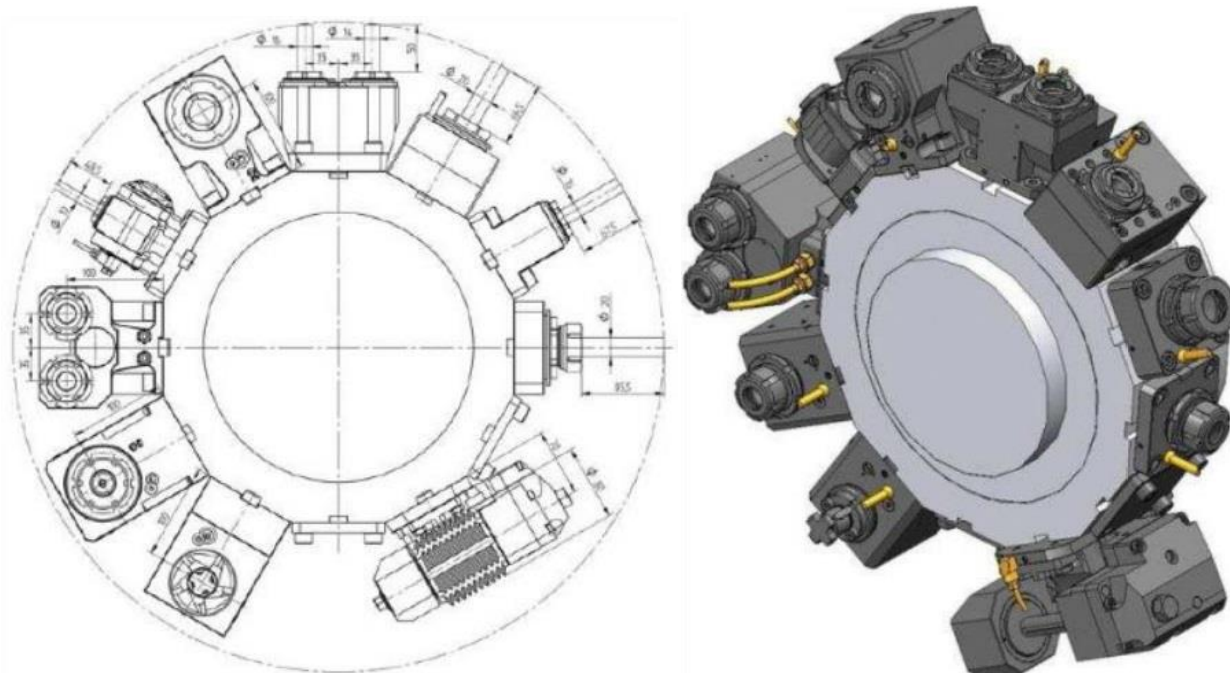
Револьверная головка BMT с блоками приводного инструмента.
